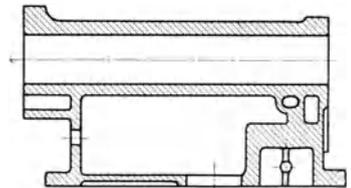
Schematischer Längsschnitt des Pumpengehäuses.
